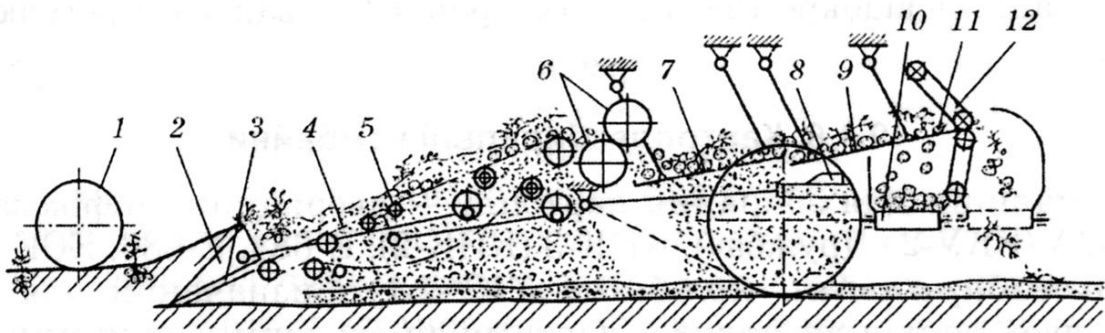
Конструктивно-технологічна схема картоплекопача – валкоутворювача УКВ-2: 1 – опорне колесо; 2 – активні боковини; 3 – леміш; 4 – основний конвеєр; 5 – струшувачі; 6 – балони-грудкоподрібнювачі; 7 – перше решето грохота; 8 – ложеутворювач; 9 – друге решето грохота; 10 – поперечний конвеєр; 11 – бадиллєвідокремлювальні тростини; 12 – бадиллєвідокремлювальні гірки
